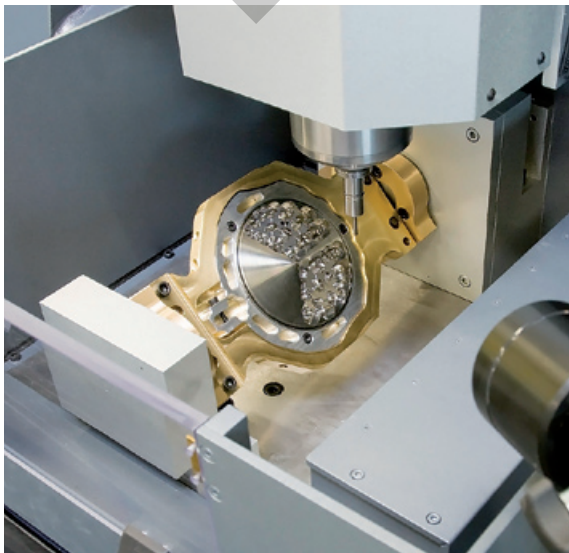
Schwenktisch für die 4-Achs-Bearbeitung.
